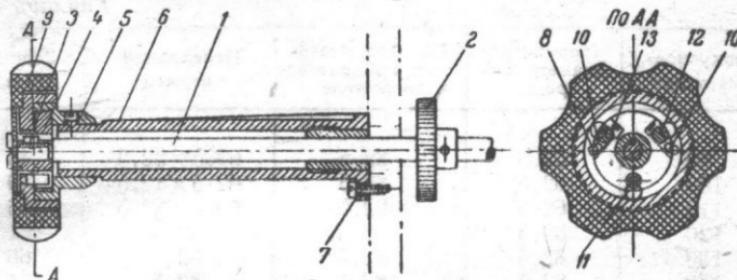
Механизм установки кадра в рамку: 1—вал; 2—шестерня; 3—шпонка; 4—поводок; 5—втулка; 6—кронштейн; 7—винт; 8—шифт; 9—рукоятка; 10, 11—пальцы; 12—ролик; 13—пружина
